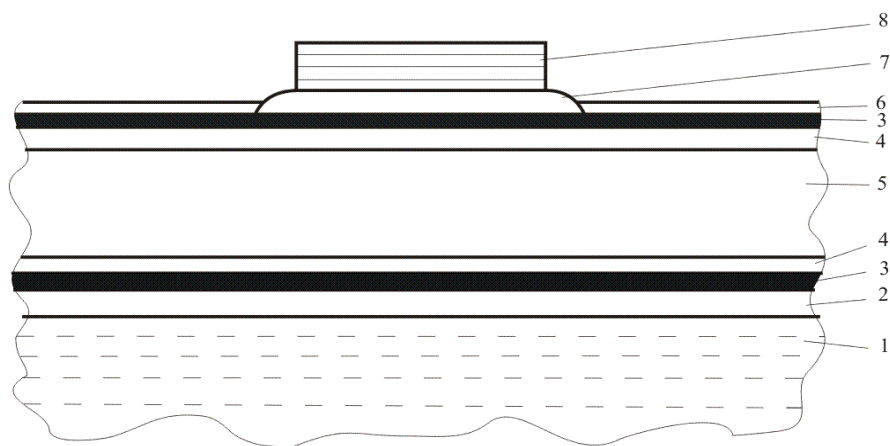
Типовая конструкция корпуса мощного СВЧ-транзистора (поперечный разрез)
